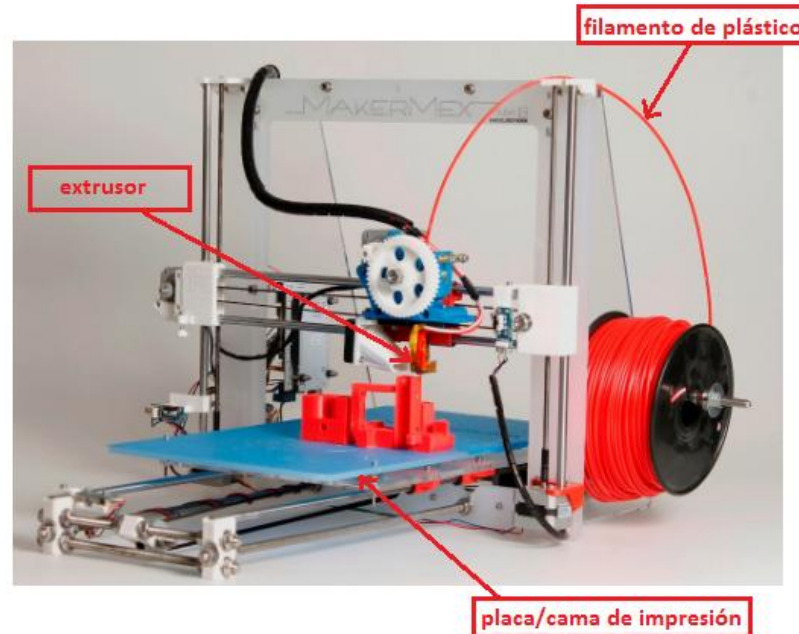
Impresión 3D mediante Modelado por Deposición Fundida (FDM). Modelo: PRUSA i3 & i3 XL MAKERMEX.
